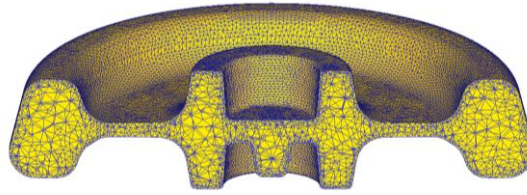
Конечно-элементная модель заготовки железнодорожного колеса (заготовка после формовочного прессы силой 100 МН).
